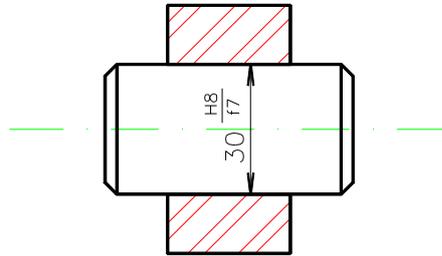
indicação de ajuste em um conjunto mecânico.
